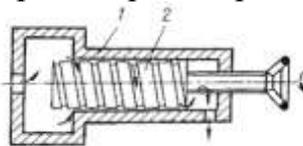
Линейный дроссель: 1 - корпус; 2 – винт
